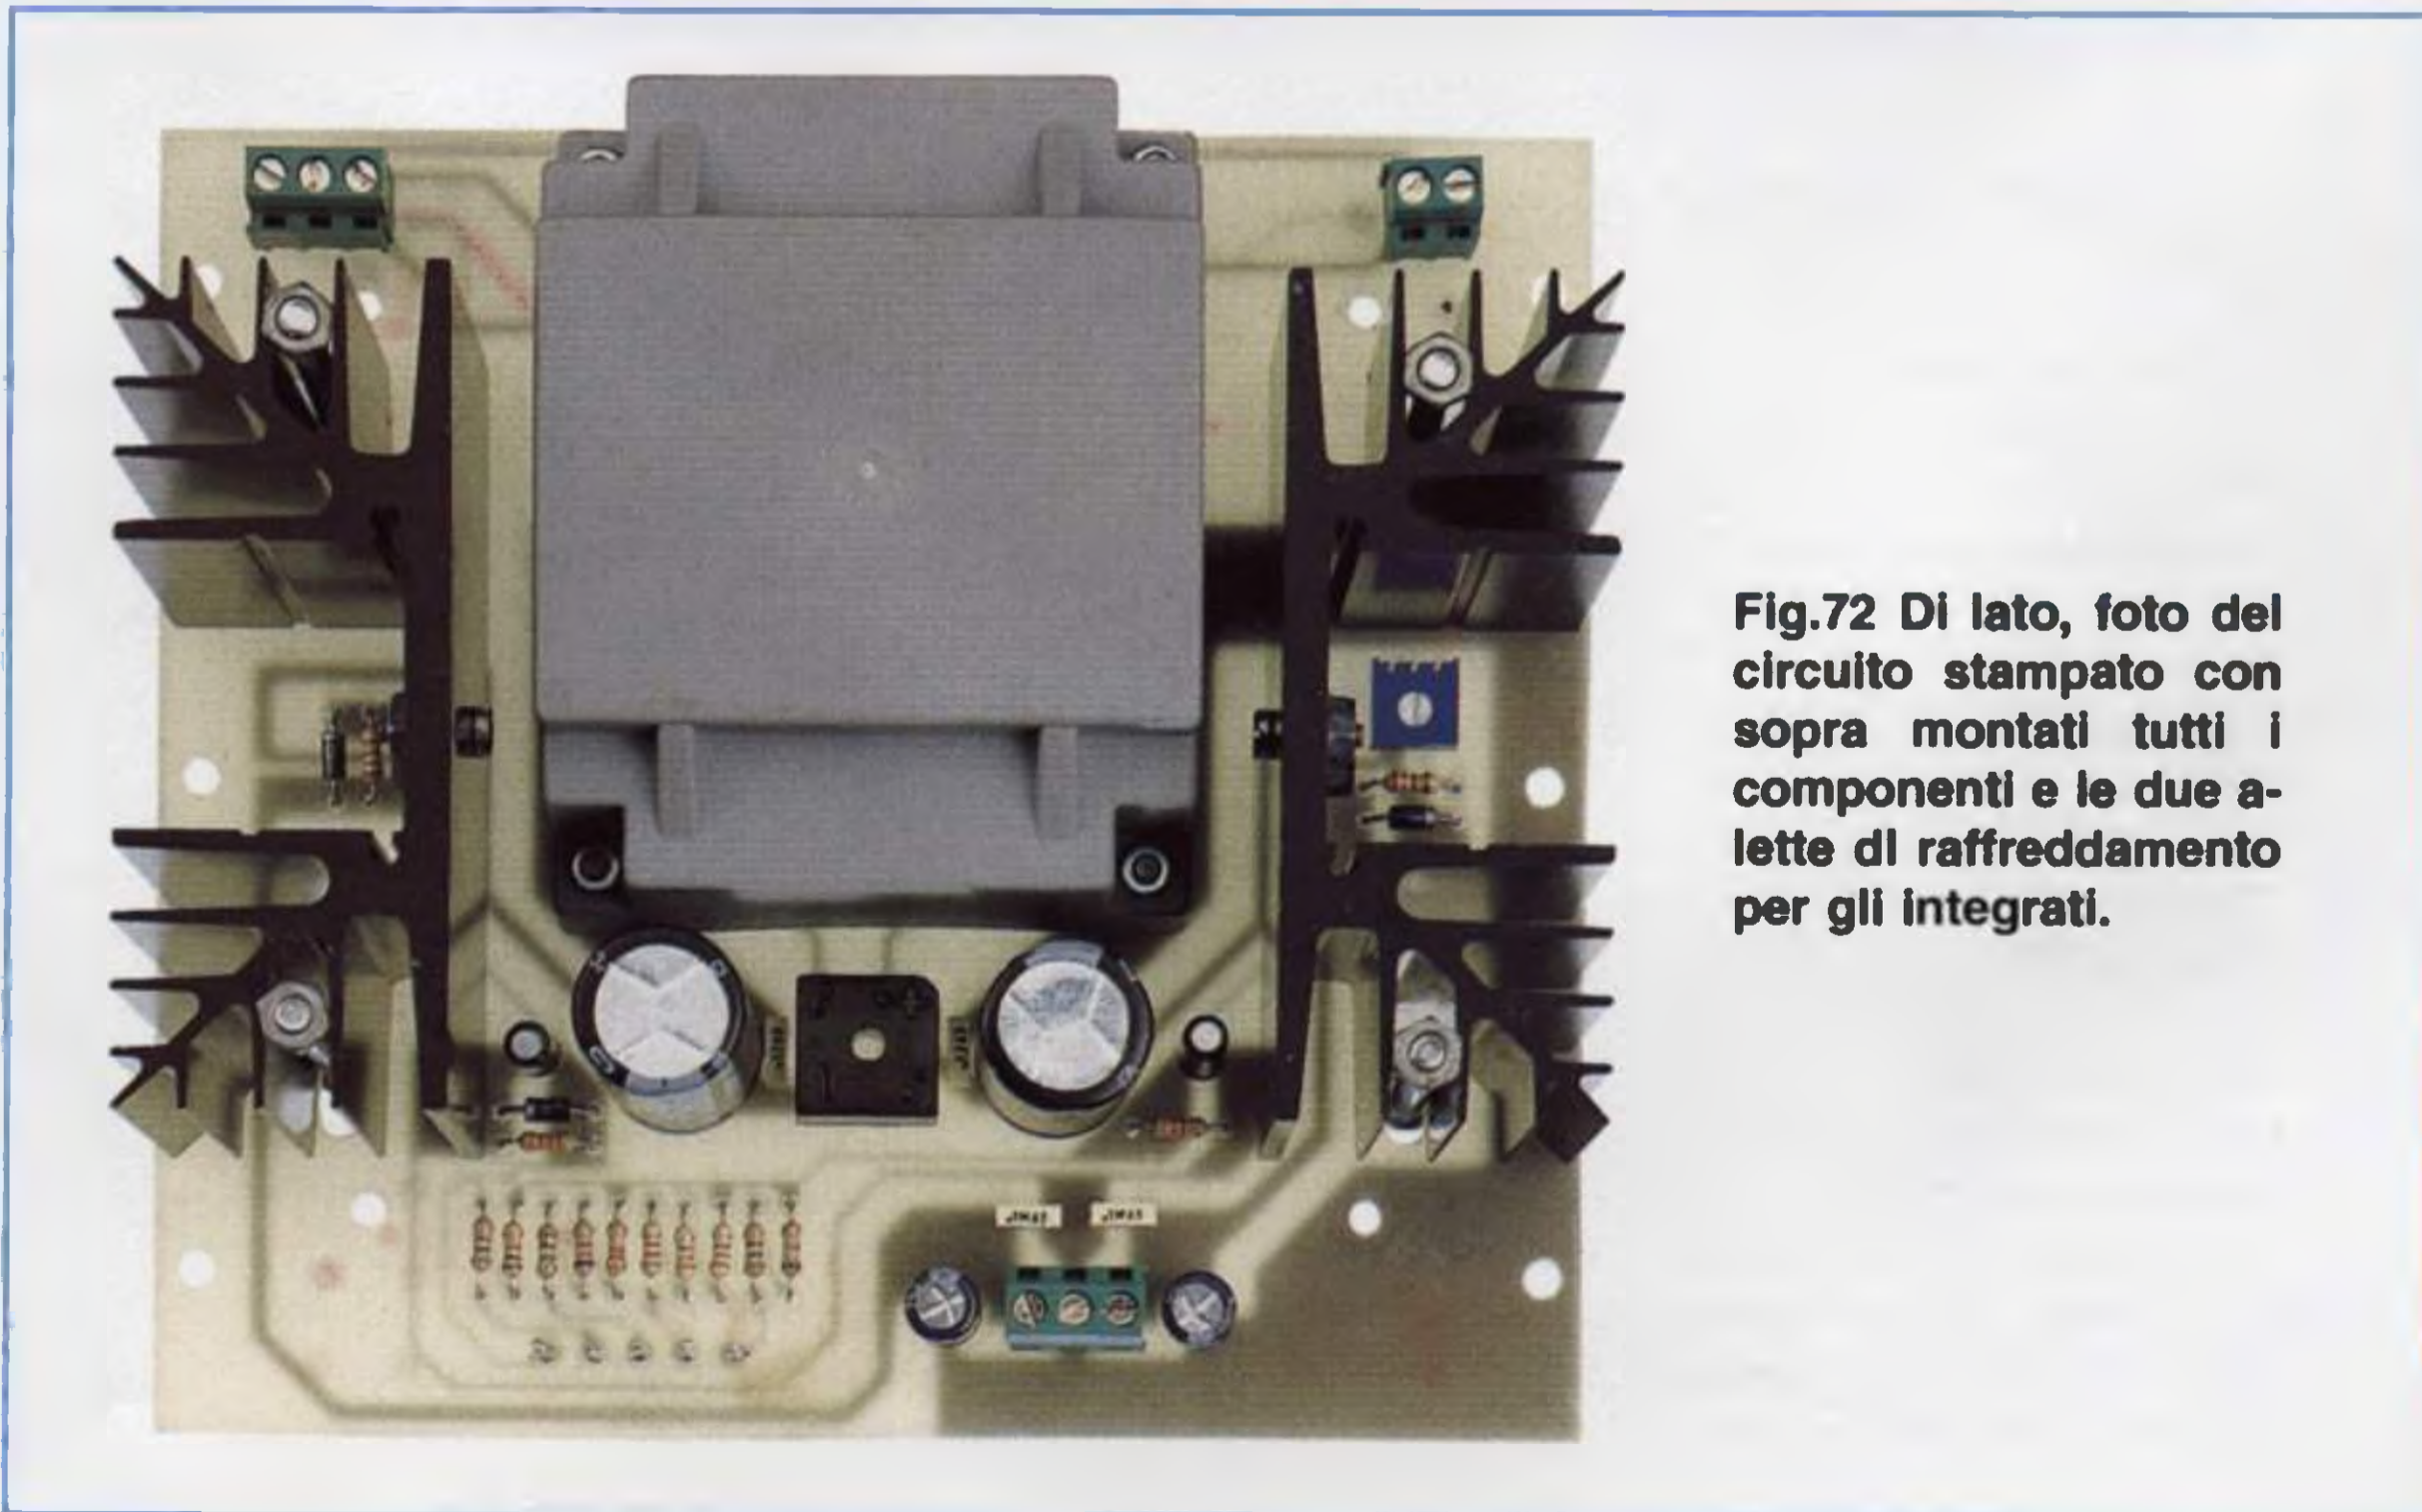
Di lato, foto del circuito stampato con sopra montati tutti i componenti e le due alette di raffreddamento per gli integrati.
